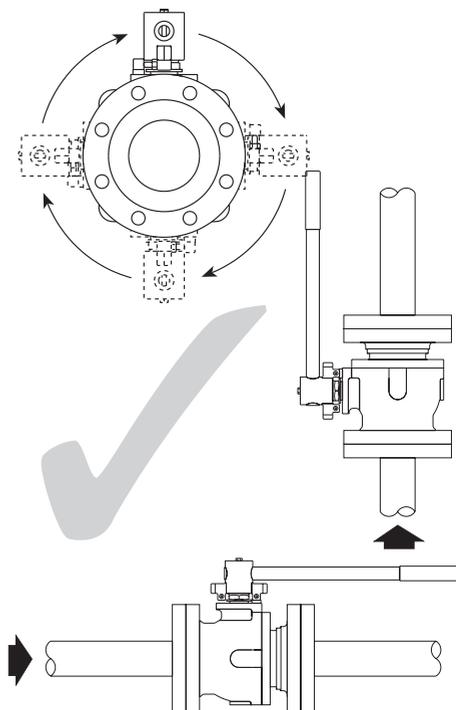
Korrekte Installation für den Betrieb mit Gas
